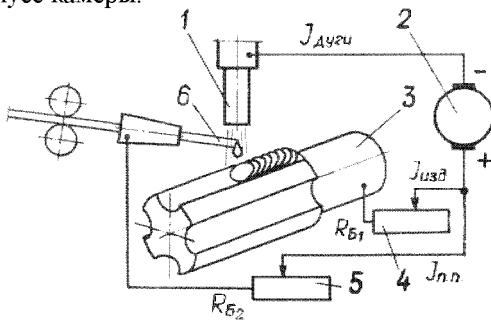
Схема наплавки в вакууме с раздельной регулировкой тепловложения в заготовку инструмента и присадочную проволоку, где: 1 – полый катод; 2 – источник питания дуги; 3 – заготовка инструмента; 4,5 – ограничительные сопротивления; 6 – присадочная проволока.
